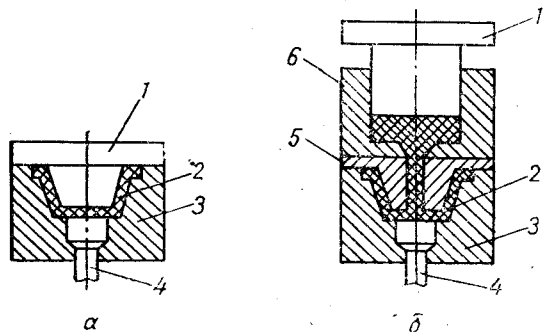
Схема прямого (а) та литтєвого (б) пресування заготовок з пластмас:
